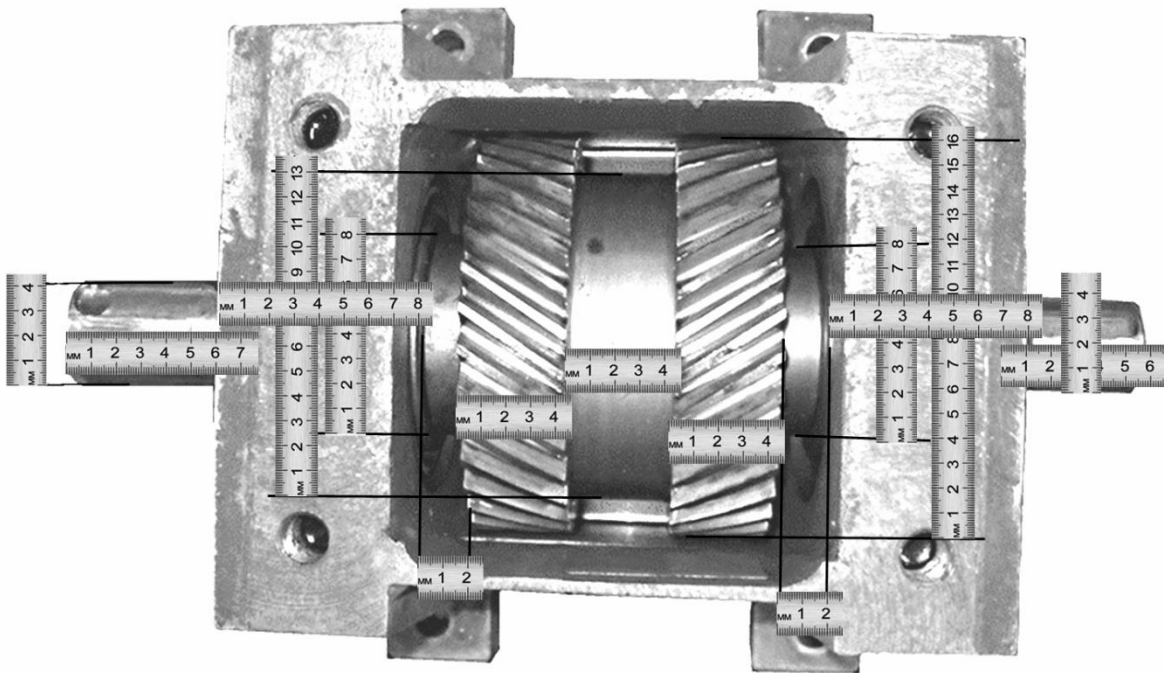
Шестерённая клетка: 1 — корпус; 2 — шестерённый валок;
